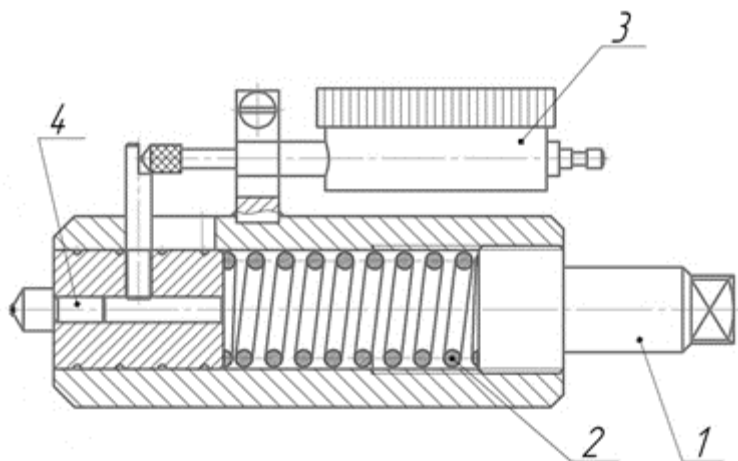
Чертеж оправки с силовым элементом в виде винтовой пружины.
